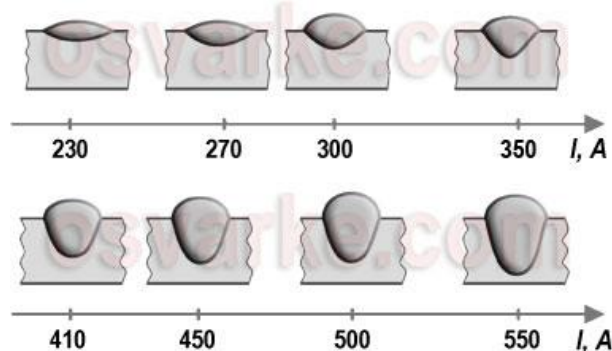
Влияние тока на форму и размеры сварного шва
